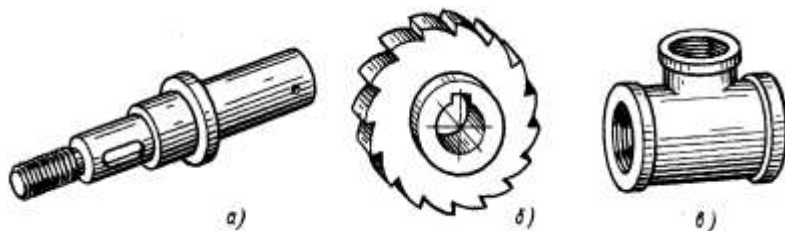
Элементы конструкции: *а* - вал; *б* - храповое колесо; *в* - тройник
